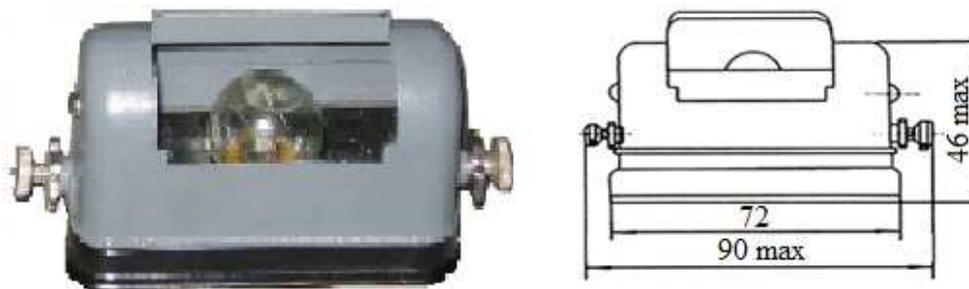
Светильник, внешний вид и габаритные размеры
